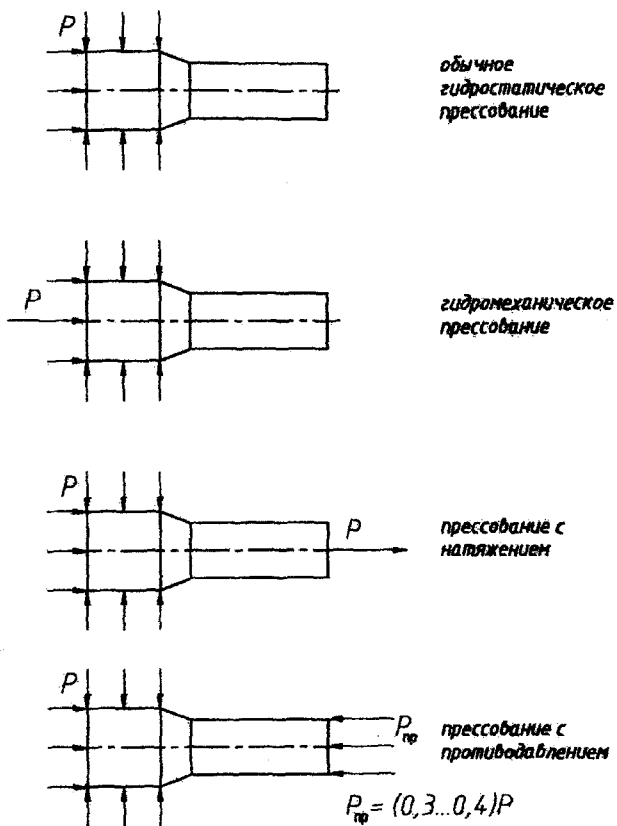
Схемы прессования с комбинированным нагружением заготовки
